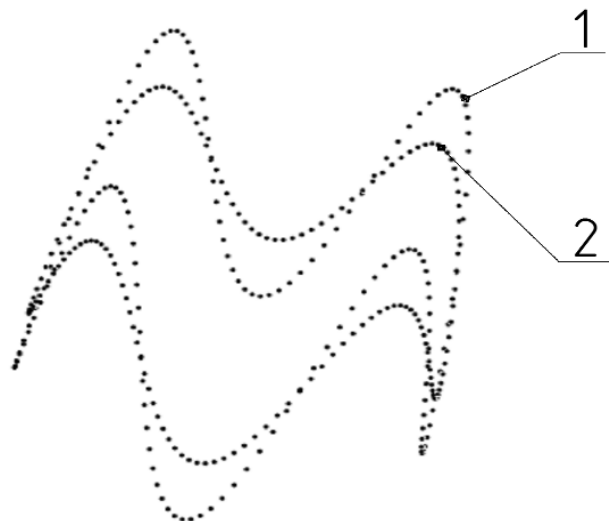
Траектории движения центра сферической фрезы: 1 – при фрезеровании профиля торцевой поверхности кулачка; 2 – при фрезеровании галтелей
